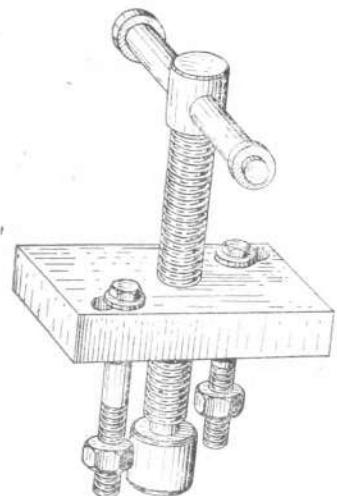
Приспособление для снятия маховика и корпуса заднего подшипника
